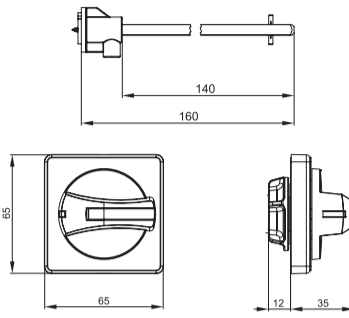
Габаритные и установочные размеры рукоятки выносной / Figure 4 – Overall and mounting dimensions of the extended handle / 4 сурет – Шығармалы тұтқаның габариттік және орнату өлшемдері
